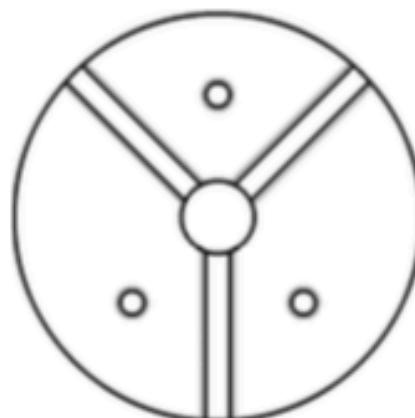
Эскиз направлений сверления отверстий с нарезанной резьбой на ручке шкалы ГИР-вольномера: отверстия для крепления диска шкалы – параллельно отверстию под ось КПЕ, радиальные отверстия для крепления ручки на оси КПЕ
